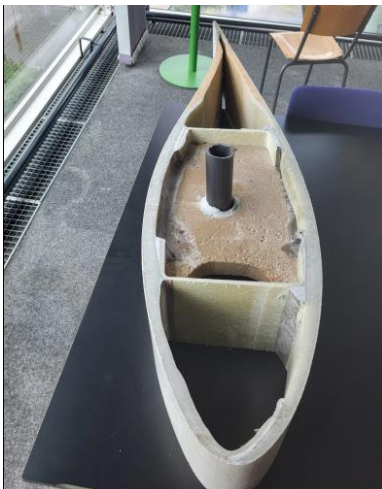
Sectie van een LM- blad met 2 lijven en een groter constructief deel.
